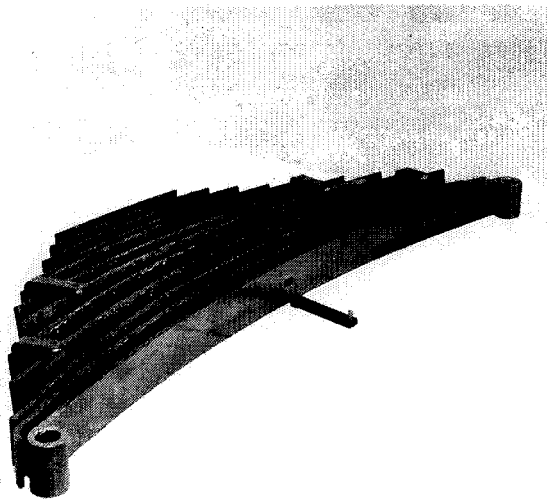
Mit einer Schraubzwinde zusammengespannte Vorderradfeder
